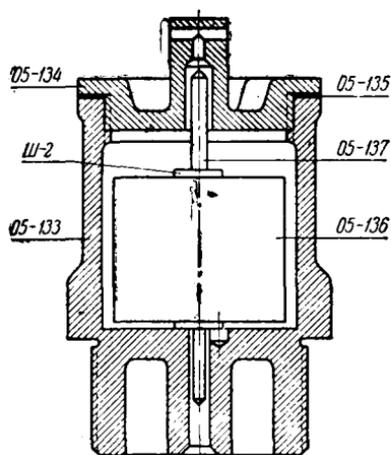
Дет. № 2513; Пробка-клапан топливного бака в сборе
